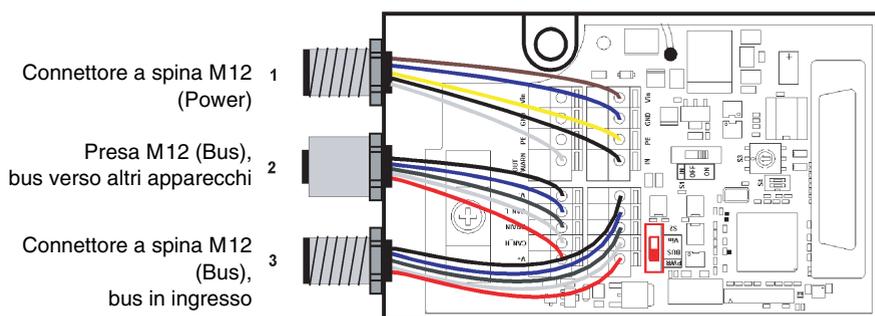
Montaggio e collegamento dei connettori M12 opzionali
